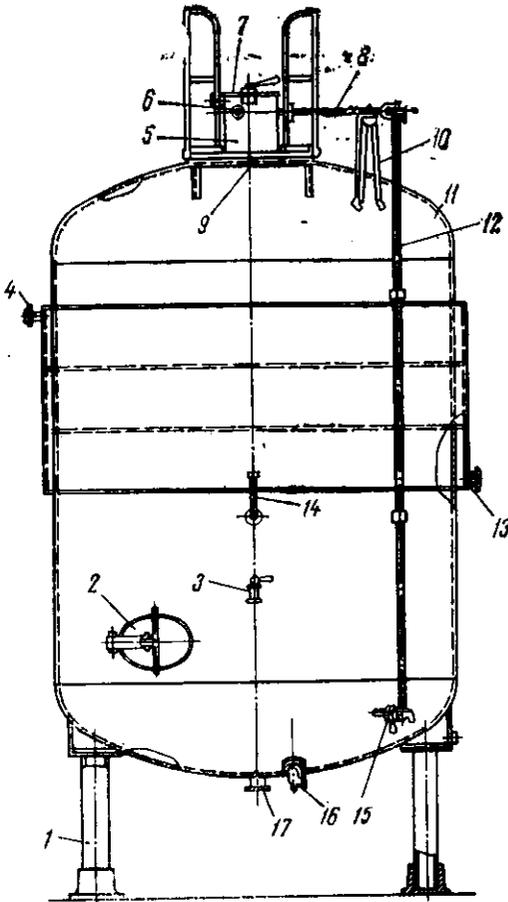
Вертикальный металлический резервуар В-694 с верхней рубашкой:
